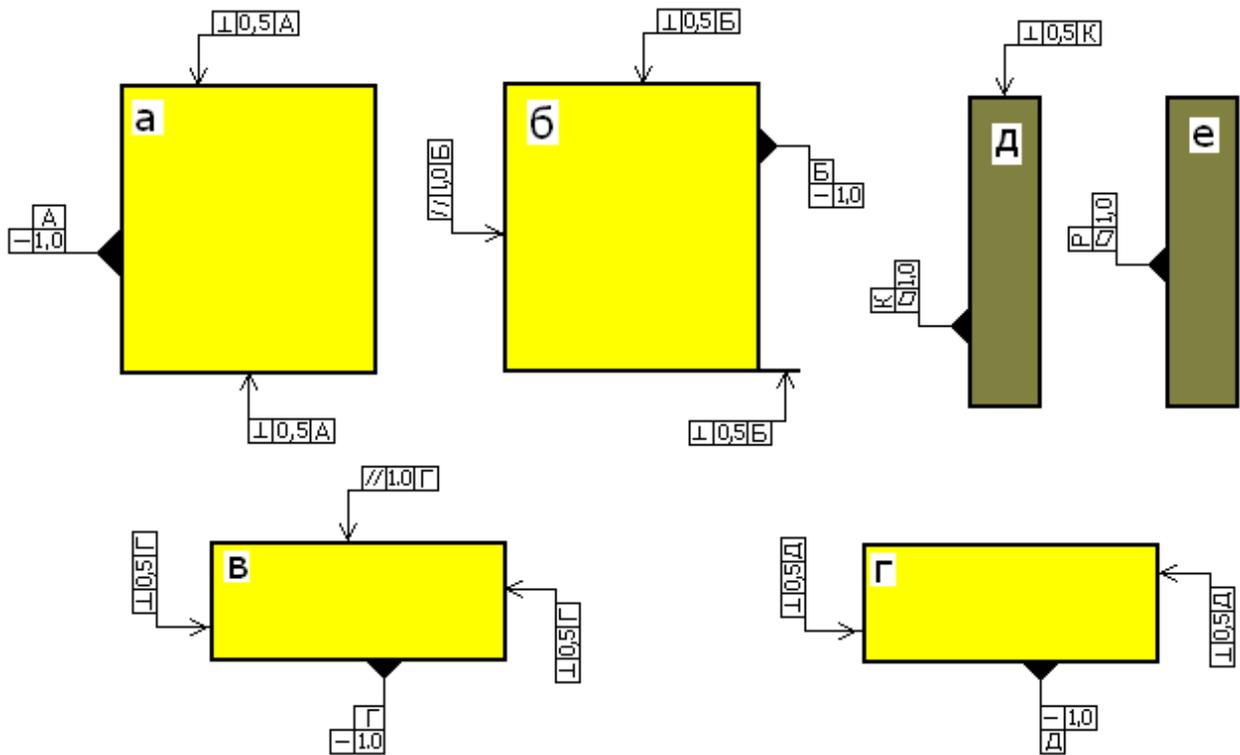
Обозначение формы, расположения поверхностей и баз:
